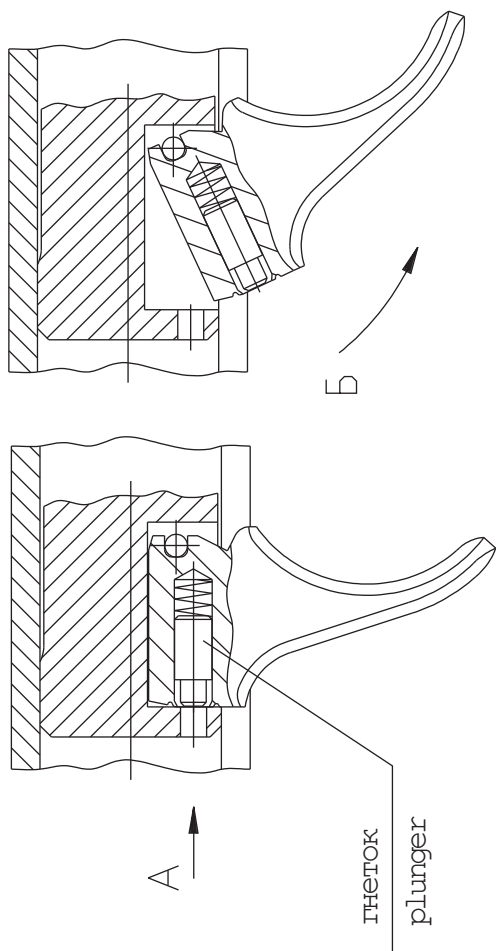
Схема разборки затвора с рукояткой.
